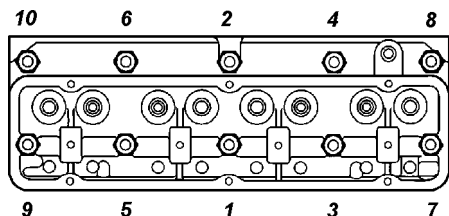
Порядок подтяжки гаек головки блока цилиндров
